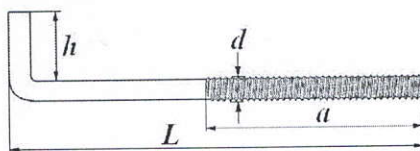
Конструкция и внешний вид винтов-костылей
